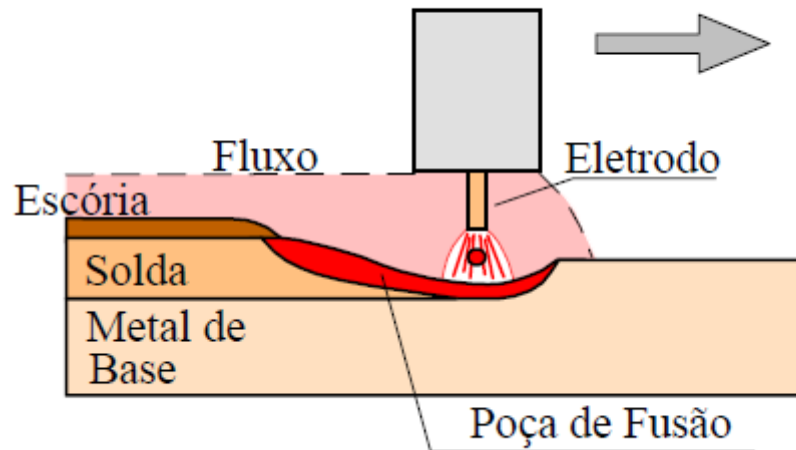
Esquemática do processo de soldagem a Arco Submerso
